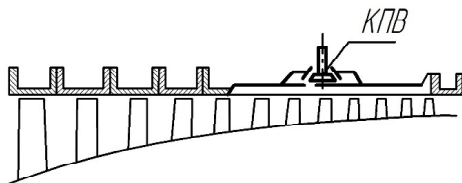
Схема газо-воздушного тракта компрессора турбовального двигателя, КПВ – клапан перепуска воздуха
